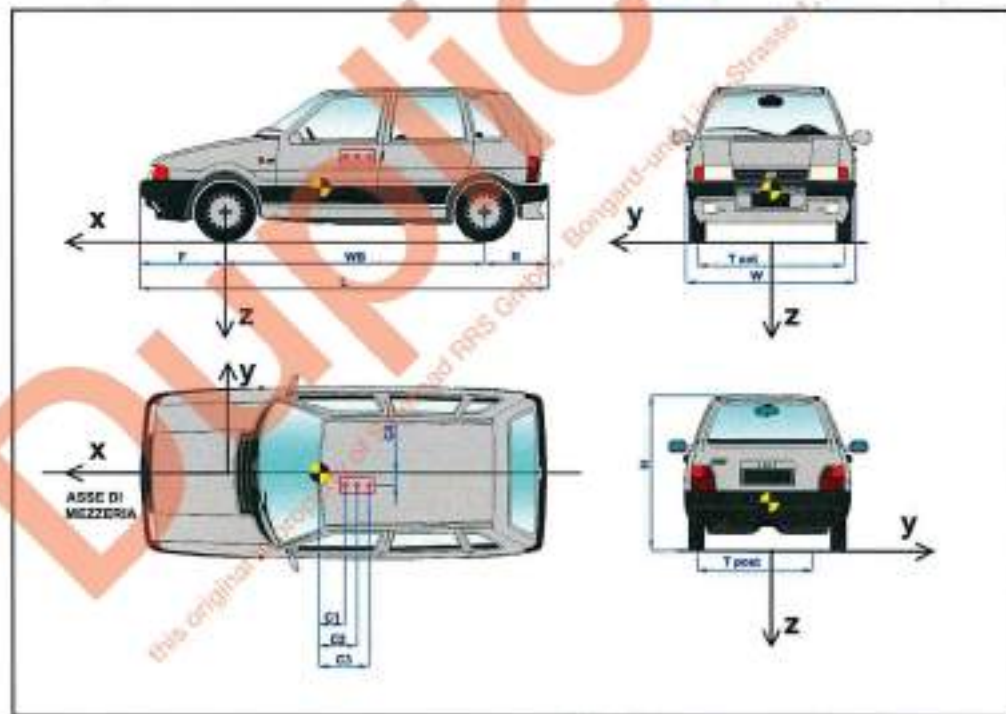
Dimensioni del veicolo – Vehicle dimensions
